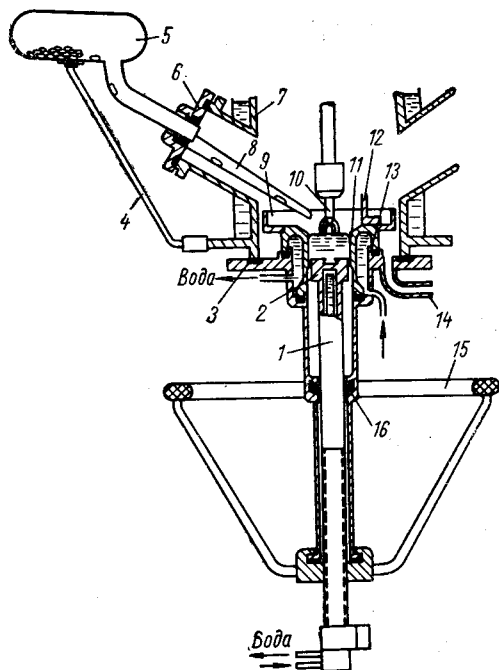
Схема приспособления для выплавки цилиндрических образцов:
